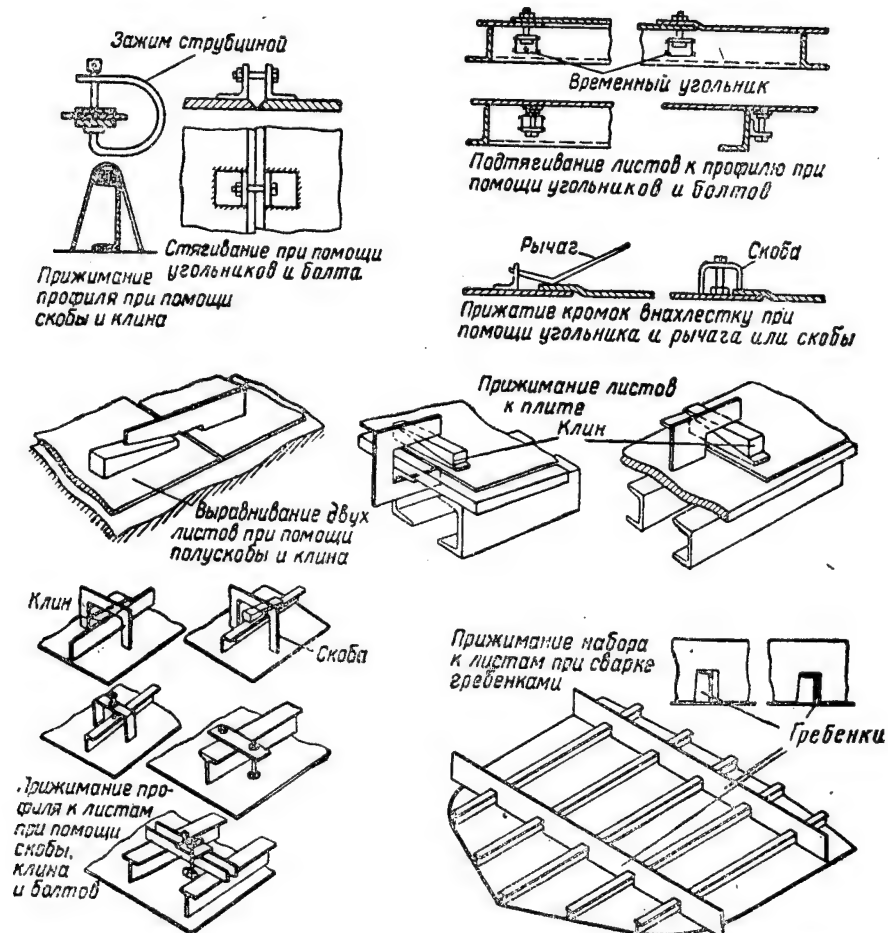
Приспособления для сборки листов и профилей под сварку
